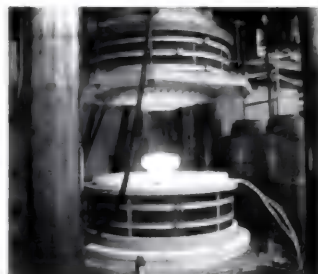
Оштампованная заготовка диска турбины ВГТД ТА18-100 из сплава ЭП975-ИД массой 50 кг. Пресс 1600 тс.
